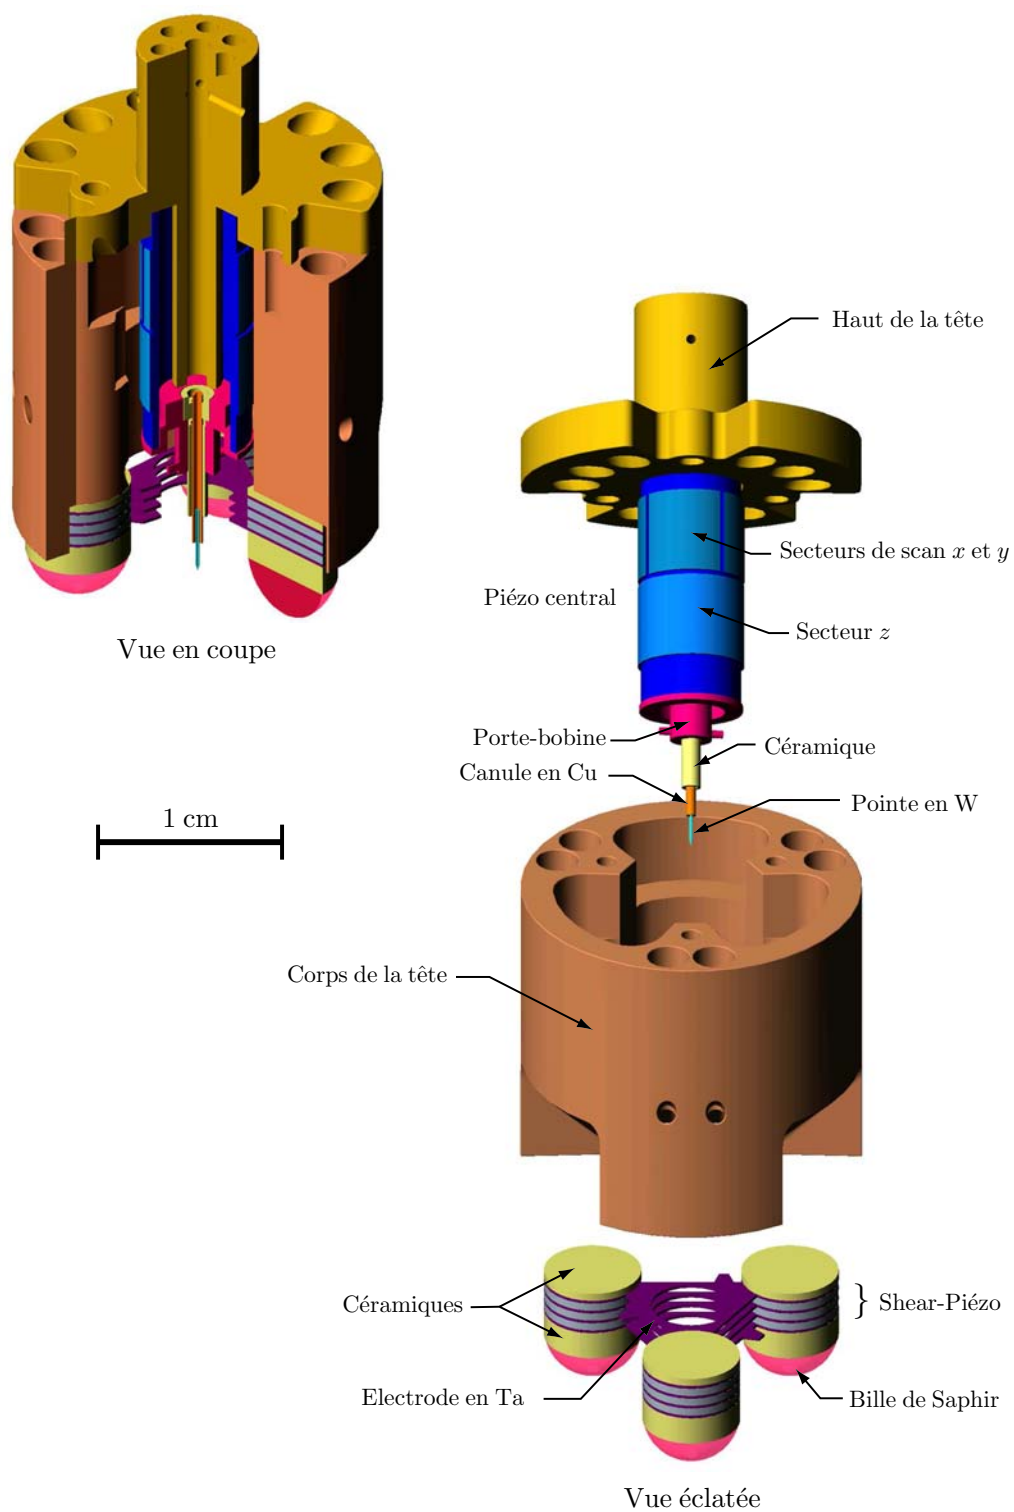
Tête STM : vue en coupe et vue éclatée.
